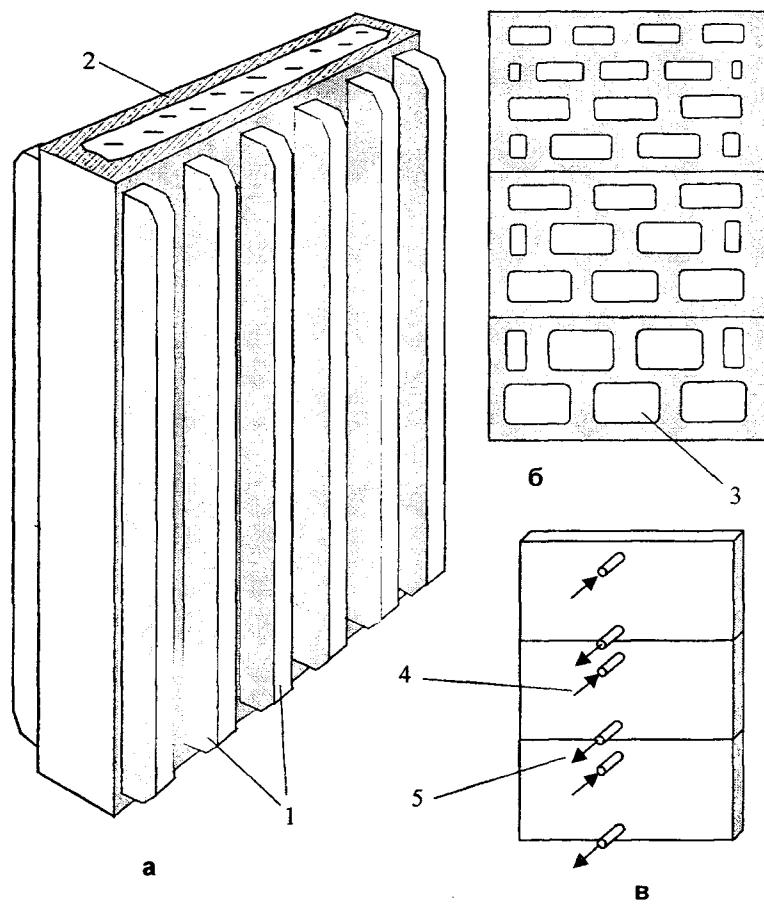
Схема поддержки слябовой заготовки брусьями (а), решётчатыми (б) и плитовыми (в) холодильниками:
